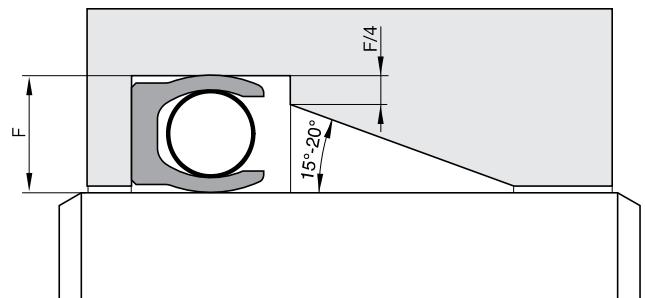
Установка закрытой посадочной канавки в режиме штока с конусным исполнением
